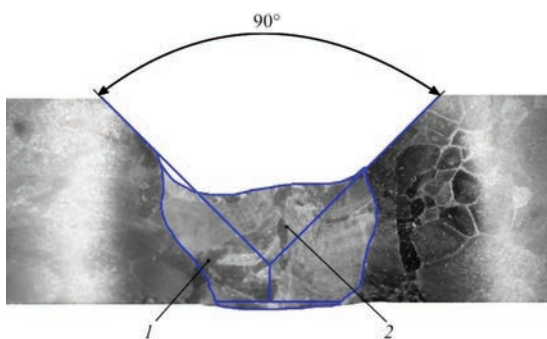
Макрошлиф соединения из сплава BT22 (после первого прохода), выполненного опытной порошковой проволокой: 1 — металл шва, 2 — металл в разделке
